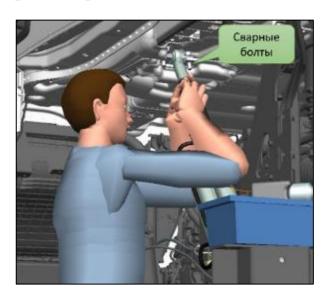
Процесс установки гидроцилиндра в сборе с болтами
